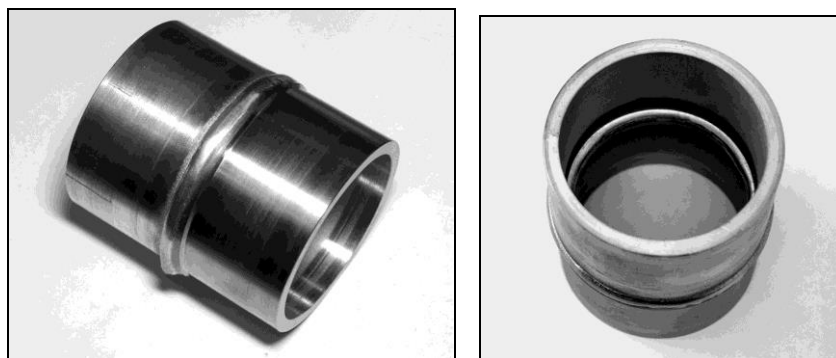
Внешний вид сварного соединения трубных заготовок АМг3+ОТ4
